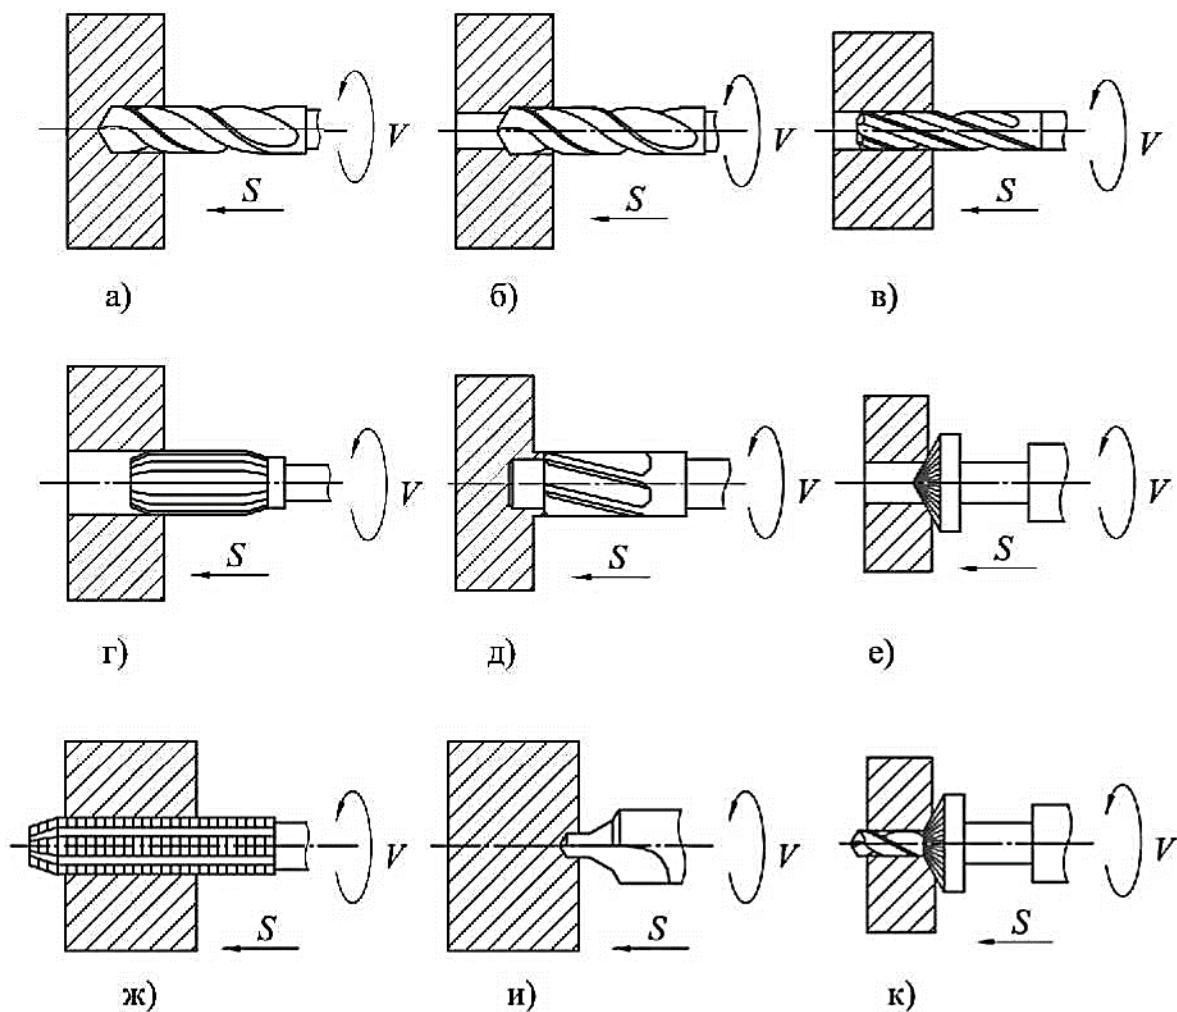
Схеми оброблення отворів на свердлильних верстатах
